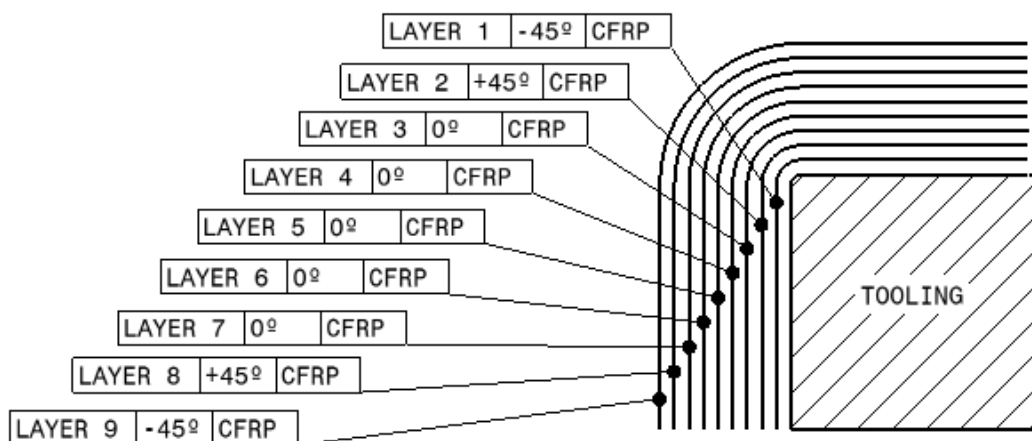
Esquema de apilado en refuerzos internos perfil en “L”
